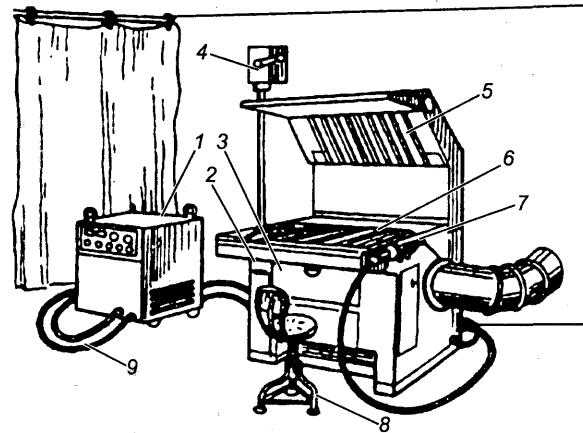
Стационарный пост для ручной дуговой сварки:
